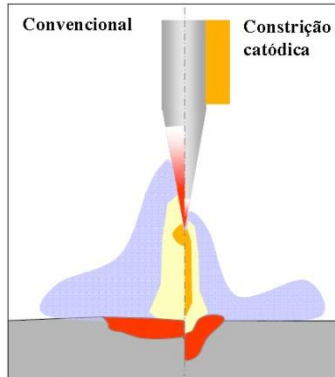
Princípio da constrição do cátodo no processo de soldagem TIG.
